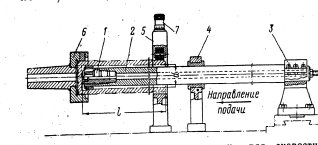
Схема насадки токарного станка для быстрого растачивания цилиндров.
